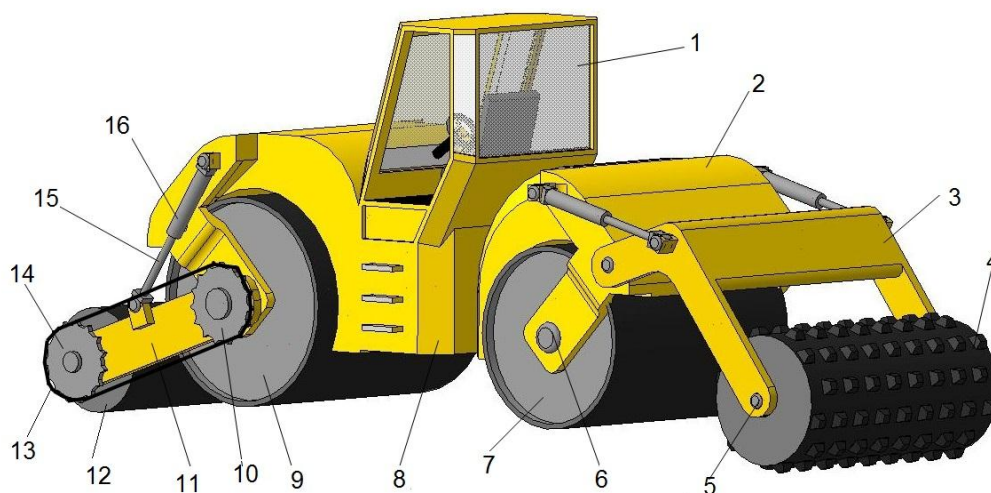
Модернизированный дорожный каток: 1 – кабина; 2 – кожух; 3 – толкающий брус для кулачкового катка; 4 – кулачковый валец; 5, 6 – поддерживающая ось; 7, 9, 12 – гладкие вальцы разного диаметра; 8 – рама; 10 – ведущая звездочка; 11 – толкающий брус; 13 – цепь; 14 – ведомая звездочка; 15 – шток главного гидроцилиндра; 16 – главный гидроцилиндр.
